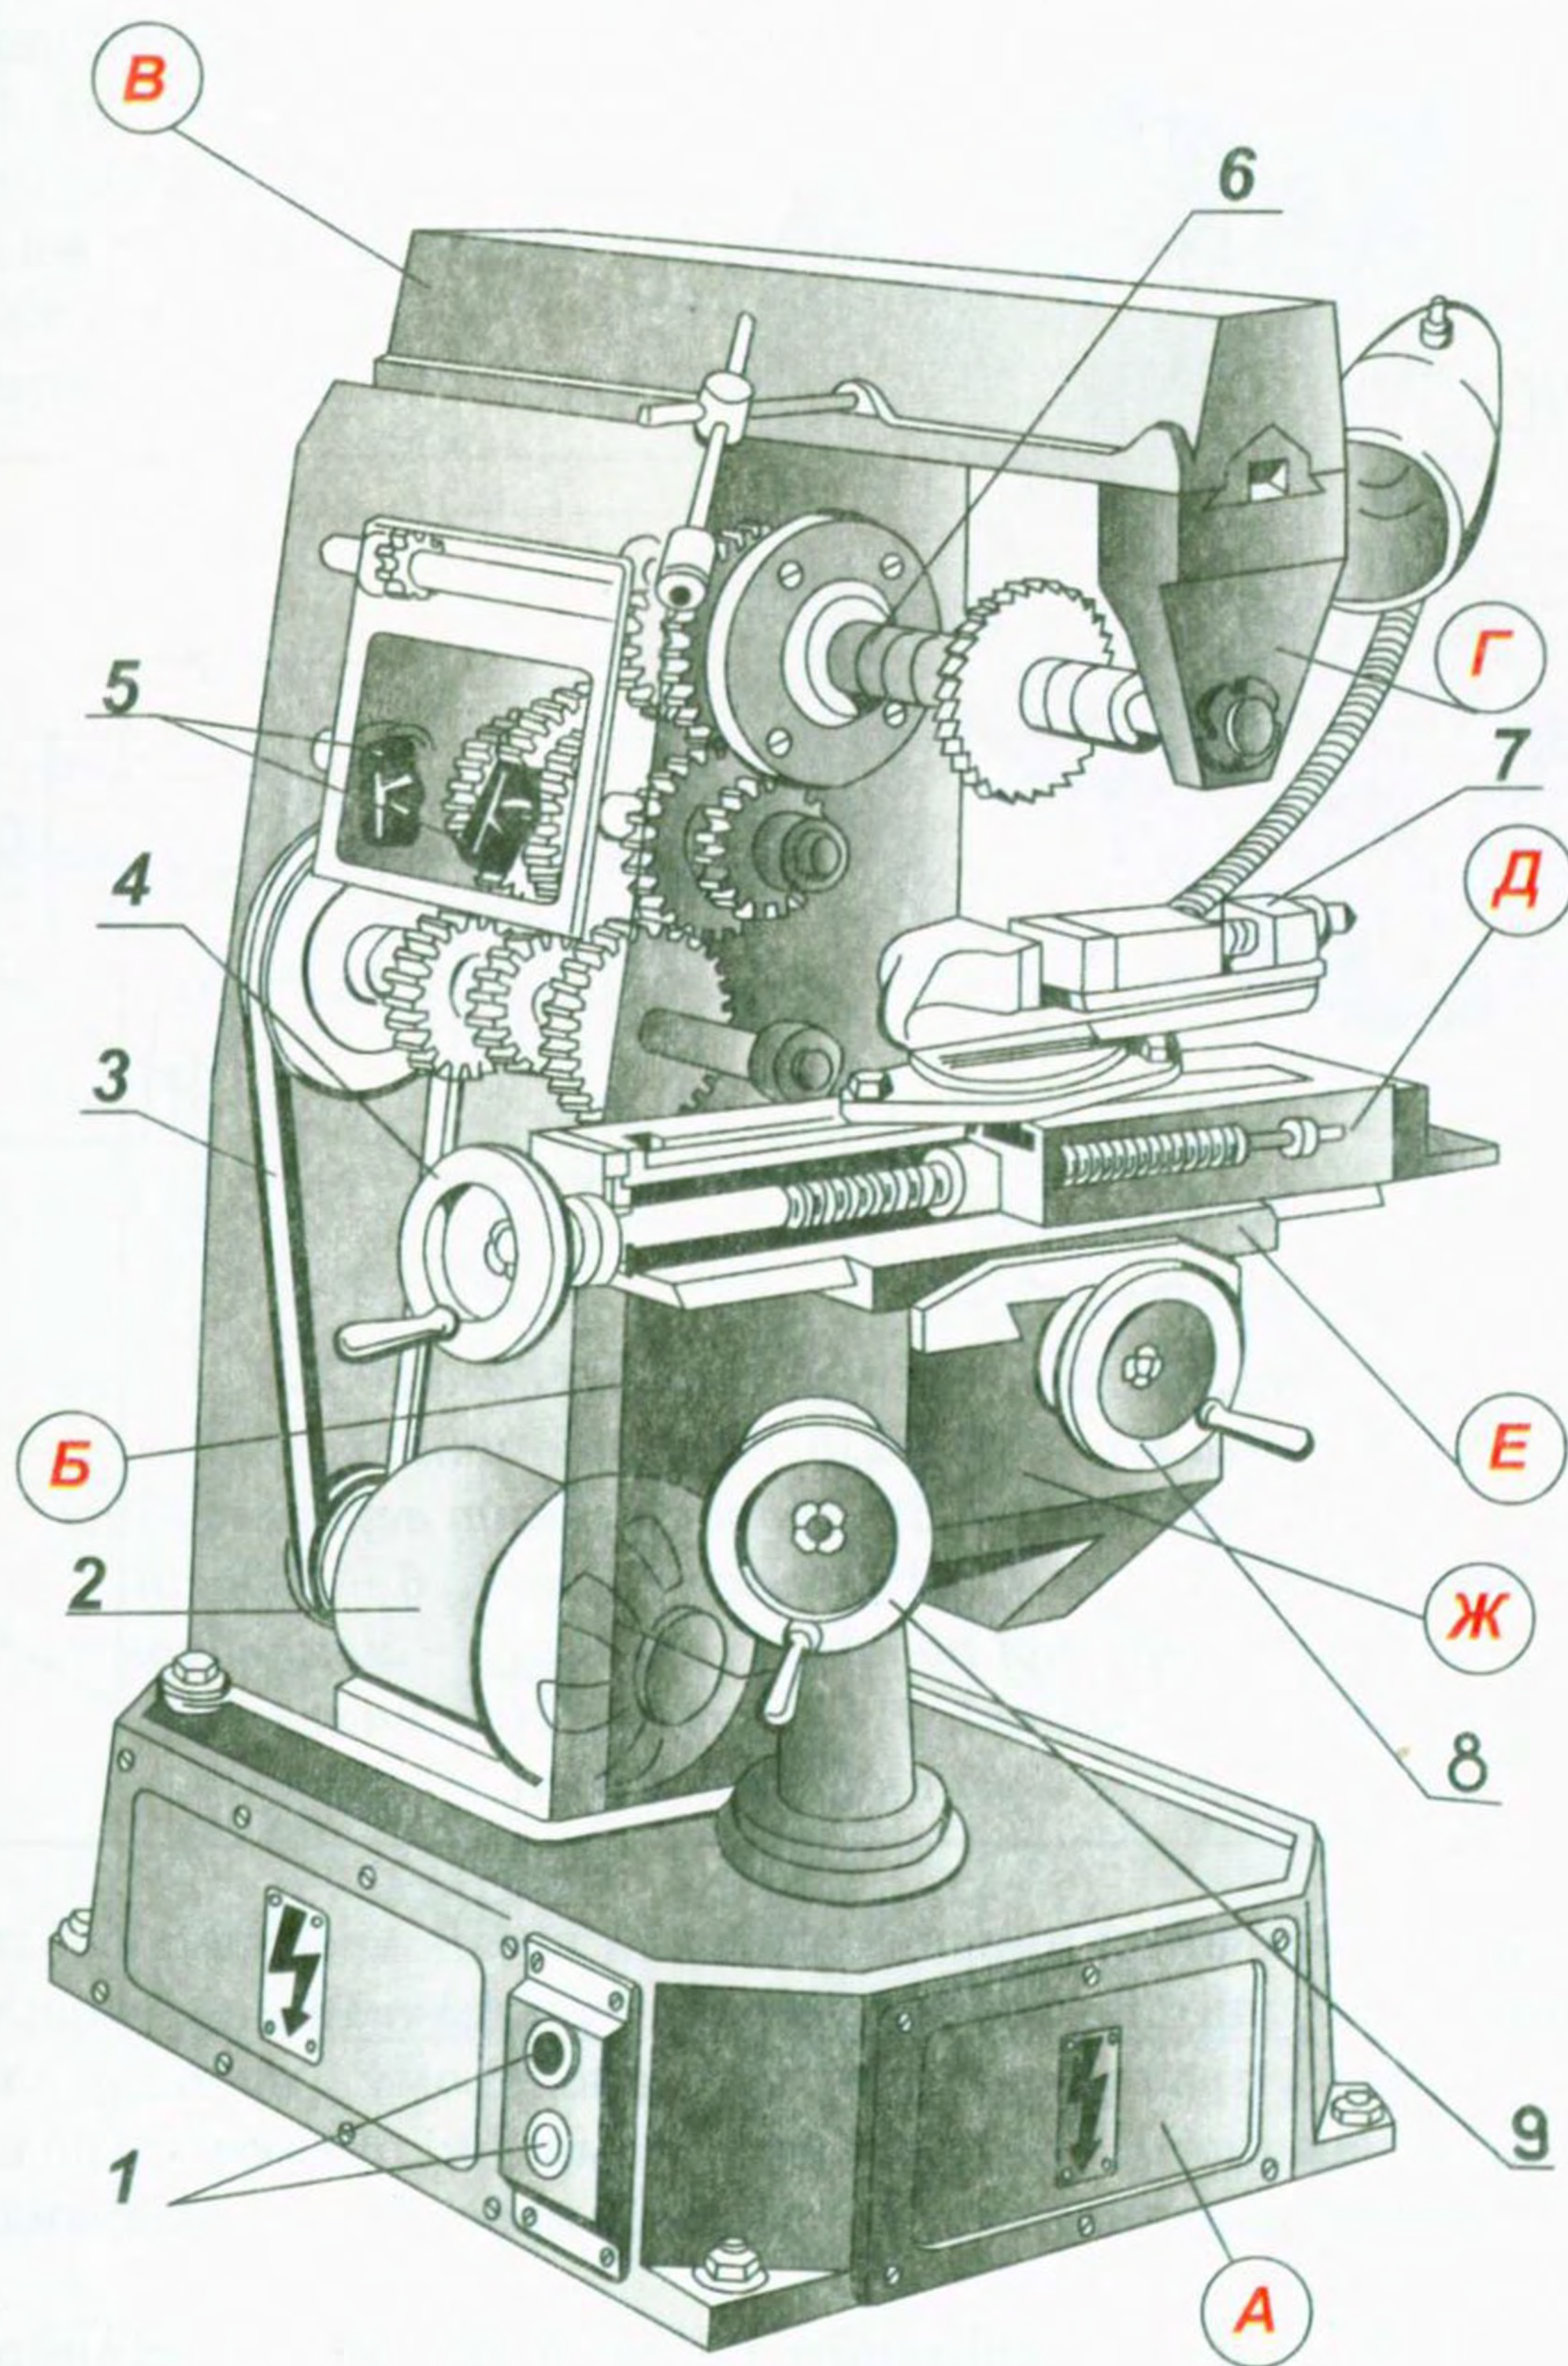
Настільний горизонтально-фрезерний верстат НГФ – 110 Ш4:
